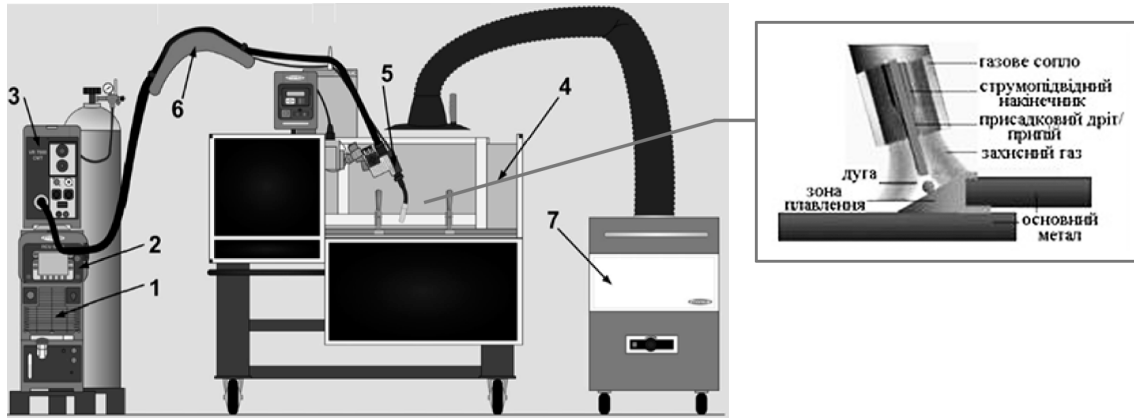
Установа для паяння та зварювання MIG/MAG методом, де 1 – джерело зварювального струму TPS 5000 CMT R; 2 – блок дистанційного керування з дисплеєм RCU 5000i; 3 – блок подачі дроту VR 7000 CMT; 4 – зварювальний стіл; 5 – зварювальний палик RobactaDriveCMT; 6 – буфер-компенсатор; 7 – мобільна система витяжки диму SuperClean 100
